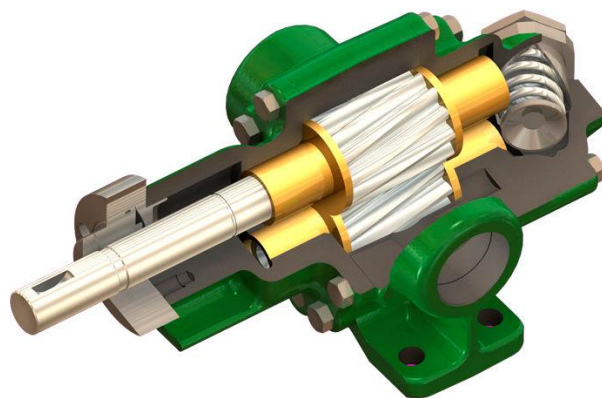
Visión 3D de una bomba de engranajes. Fuente: Direct industry
